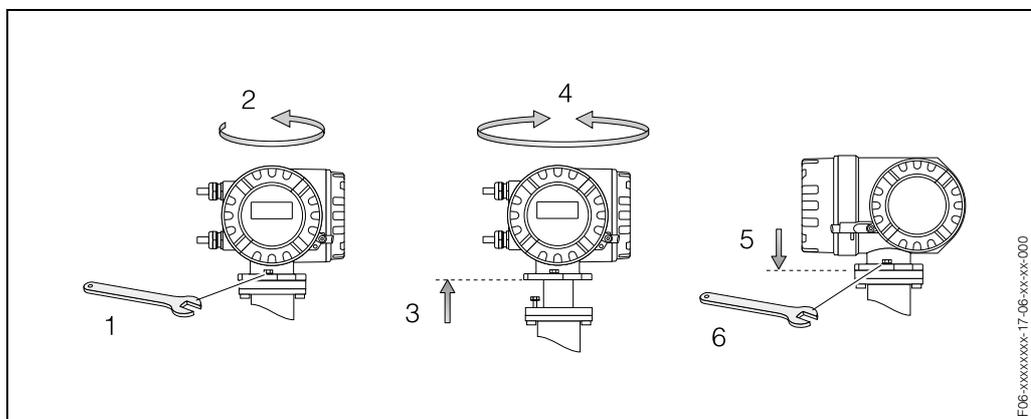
Поворот корпуса преобразователя (в алюминиевом рабочем корпусе)
